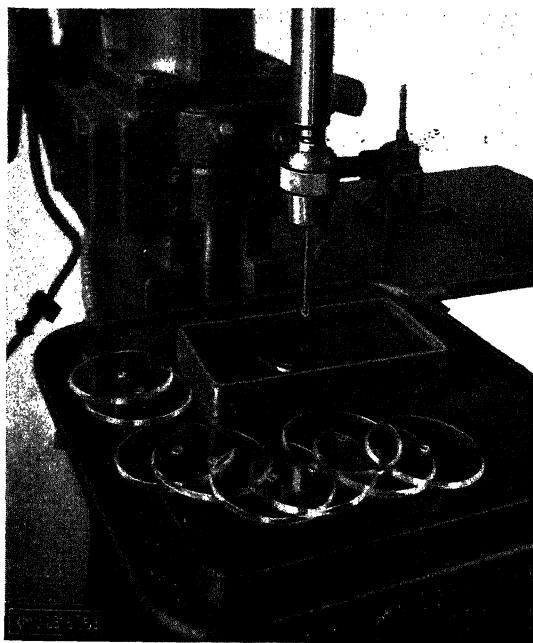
Aufbohren von Schalterglasplatten mit Widiawerkzeugen.
